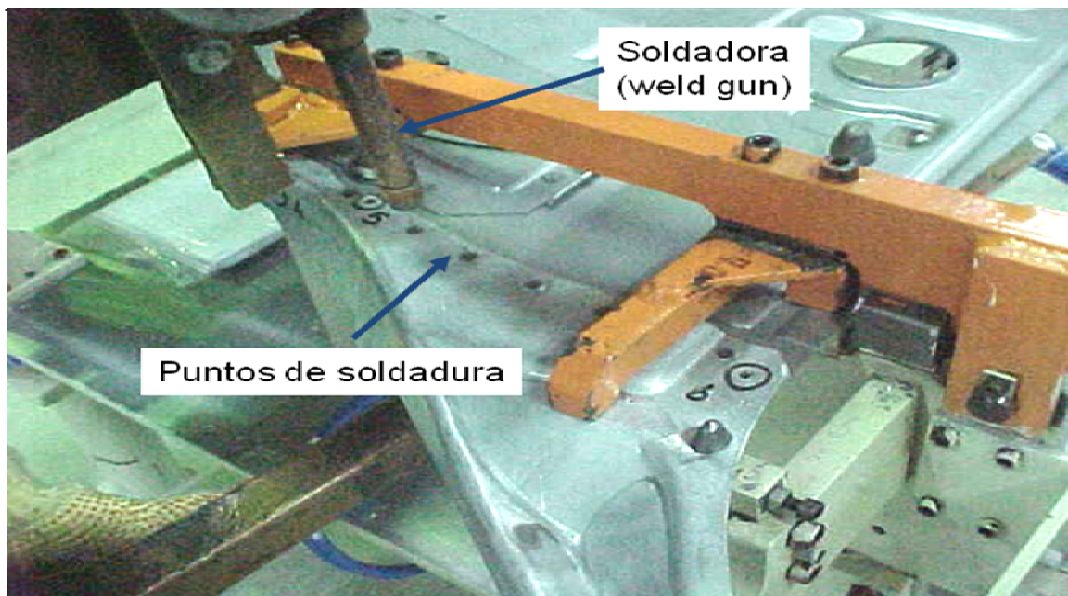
Desarrollo del proceso de soldadura
